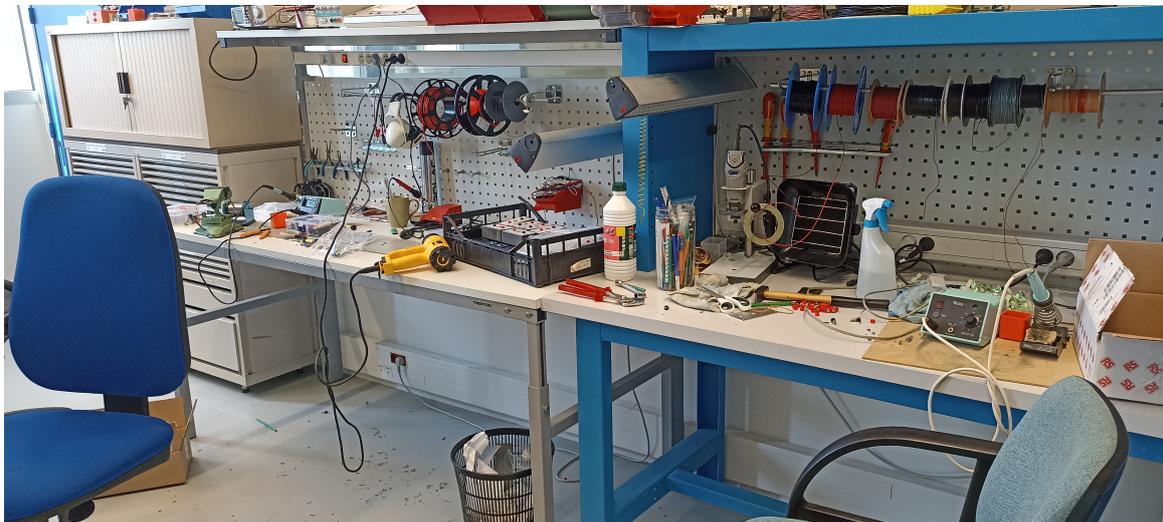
Photographie de l'atelier de soudure.
